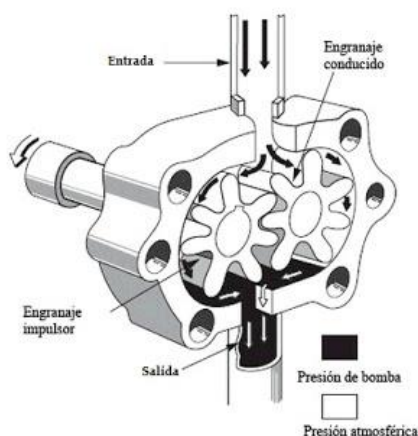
Esquema de una bomba hidráulica con engranajes externos
